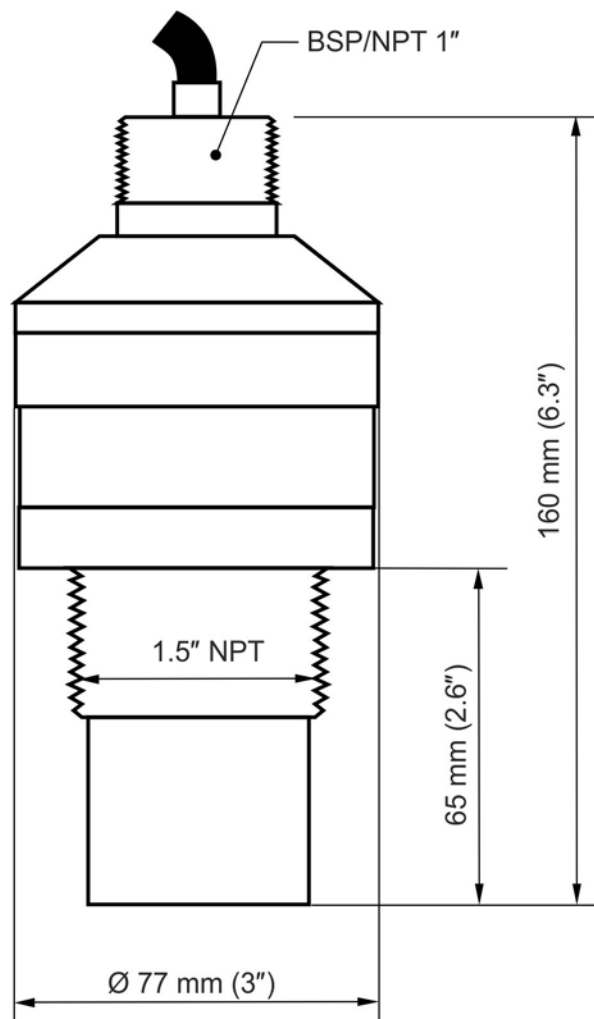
Abmessungen i-Sensor Typ 03 und Typ 06 mit Einbaugewinde kabelseitig und optionalem Frontgewinde
